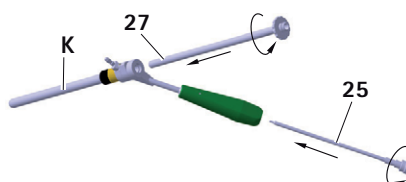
Montagem da bucha de guia Ø 3,5 mm/4,0 mm
